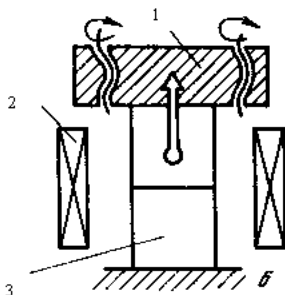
Схема диффузионной сварки принудительным деформированием:
